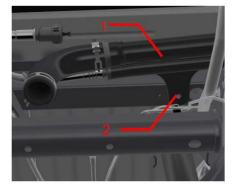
Distacco del bocchettone di immissione del carburante dal pavimento
